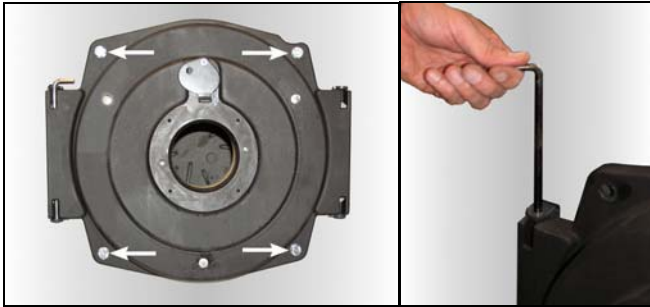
Entfernen Sie zunächst die vier M10 Befestigungsschrauben der Kesseltür und ziehen danach die Scharnierstange nach oben heraus, anschließend demontieren Sie die Kesseltür.
